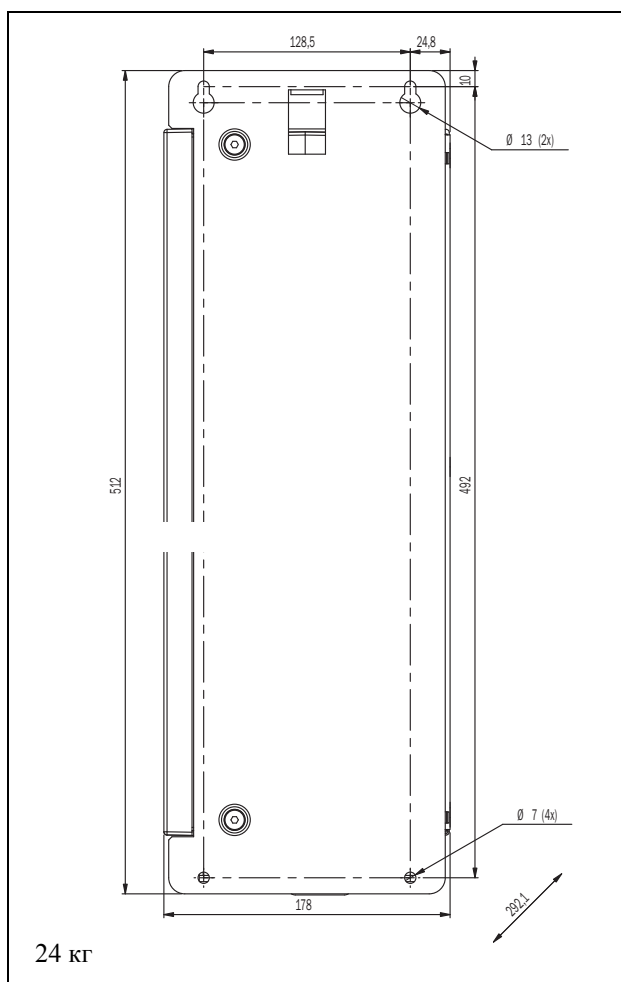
Устройство Emotron FDU моделей 48/52-026 – 046 (Типоразмер корпуса C)
